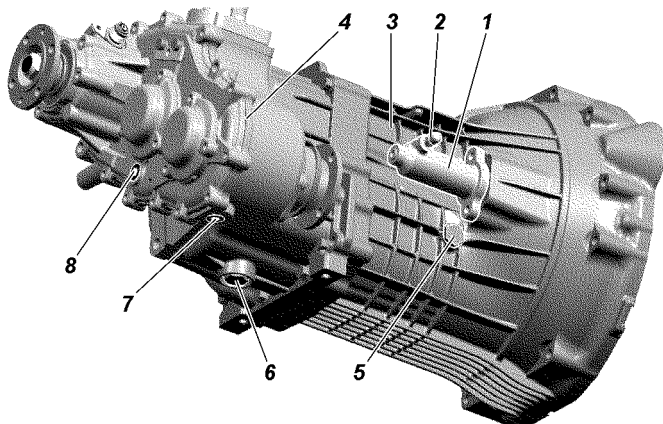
Рабочий цилиндр выключения сцепления, пятиступенчатая коробка передач и раздаточная коробка:
